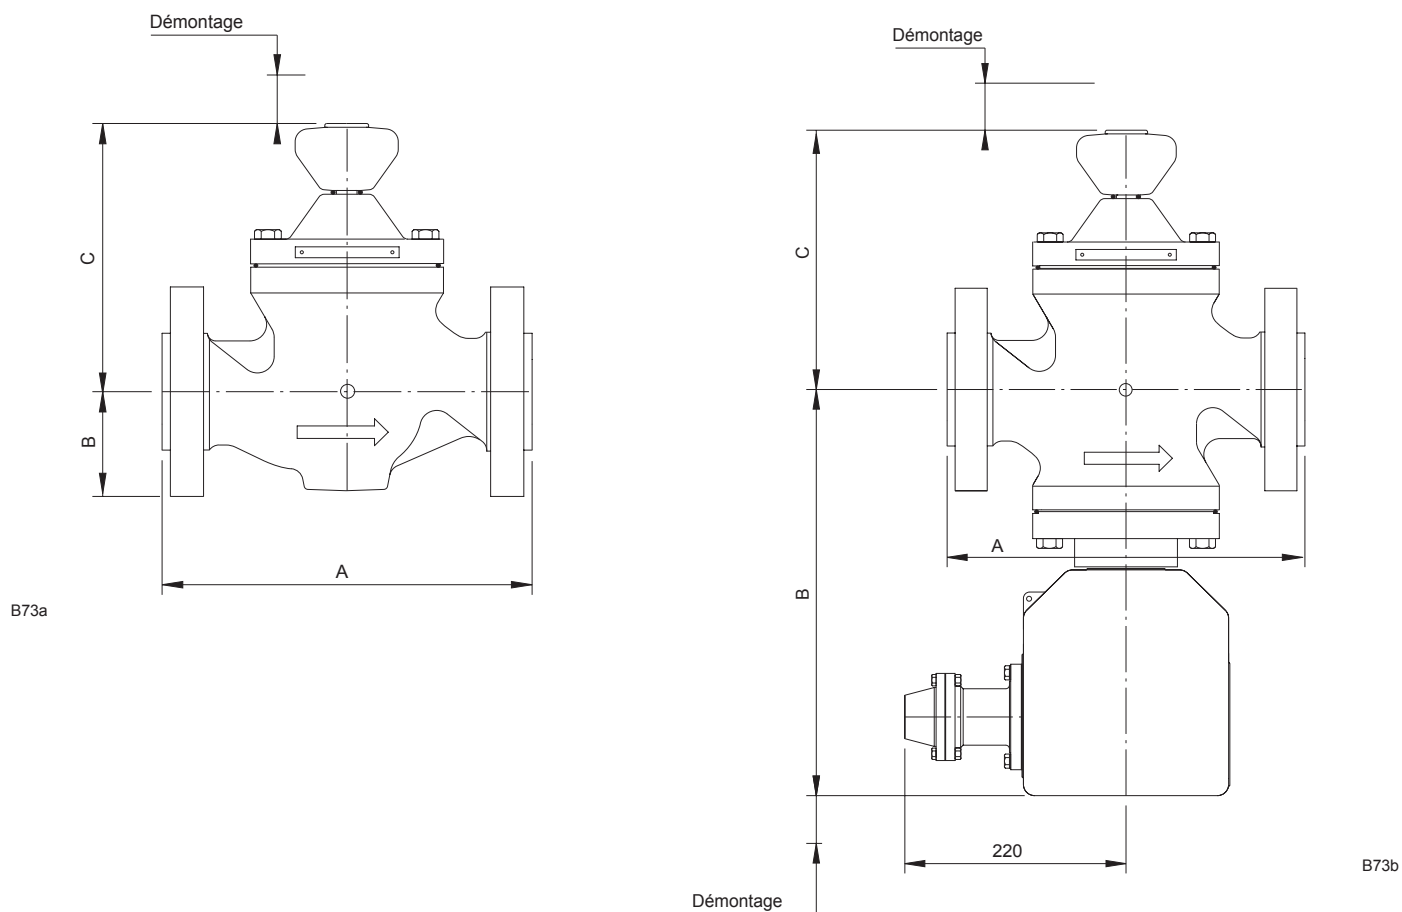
Dimensions des Vannes de Laminage Types BLE et BLX
